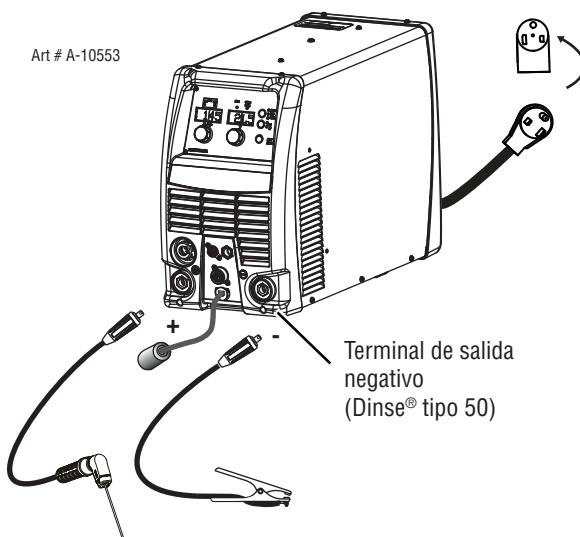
Configuración según la polaridad inversa de soldadura STICK mostrada.
